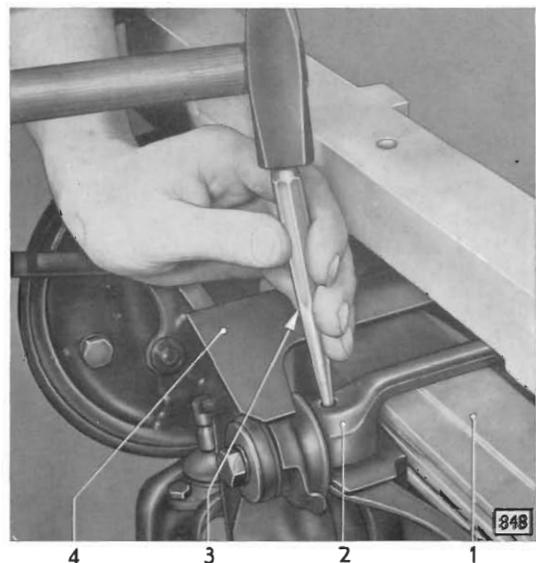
Sechskantschrauben des unteren Lenkers mit einem Dorn herausschlagen
